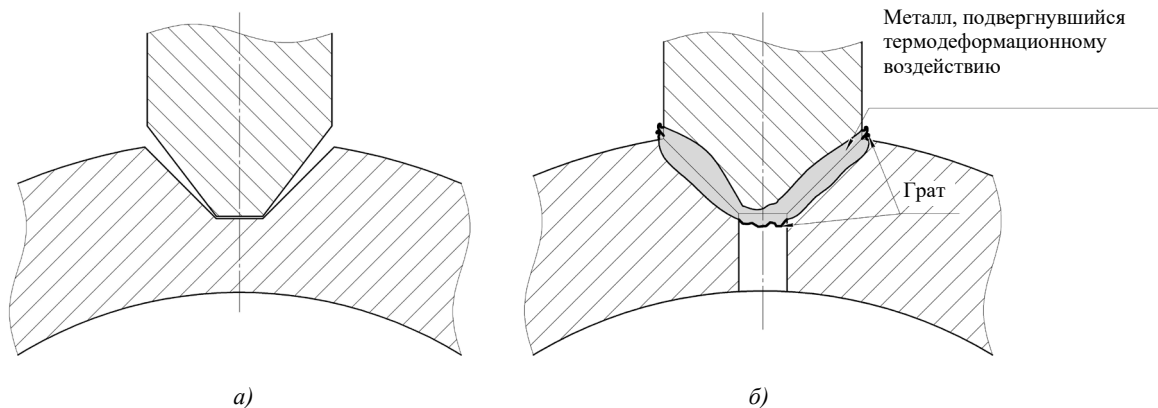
Штуцерный узел: *a* — форма контактирующей поверхности; *б* — выполненное сварное соединение
